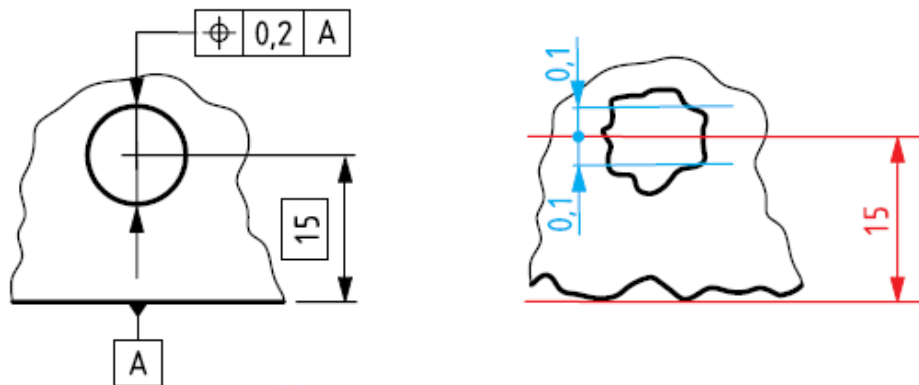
Positionstolerierung eines abgeleiteten Geometrieelementes zu einer Fläche [Nie12]
